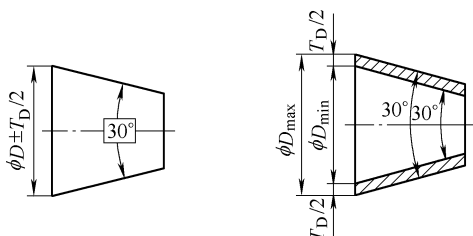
给定圆锥直径公差的基本锥度法
